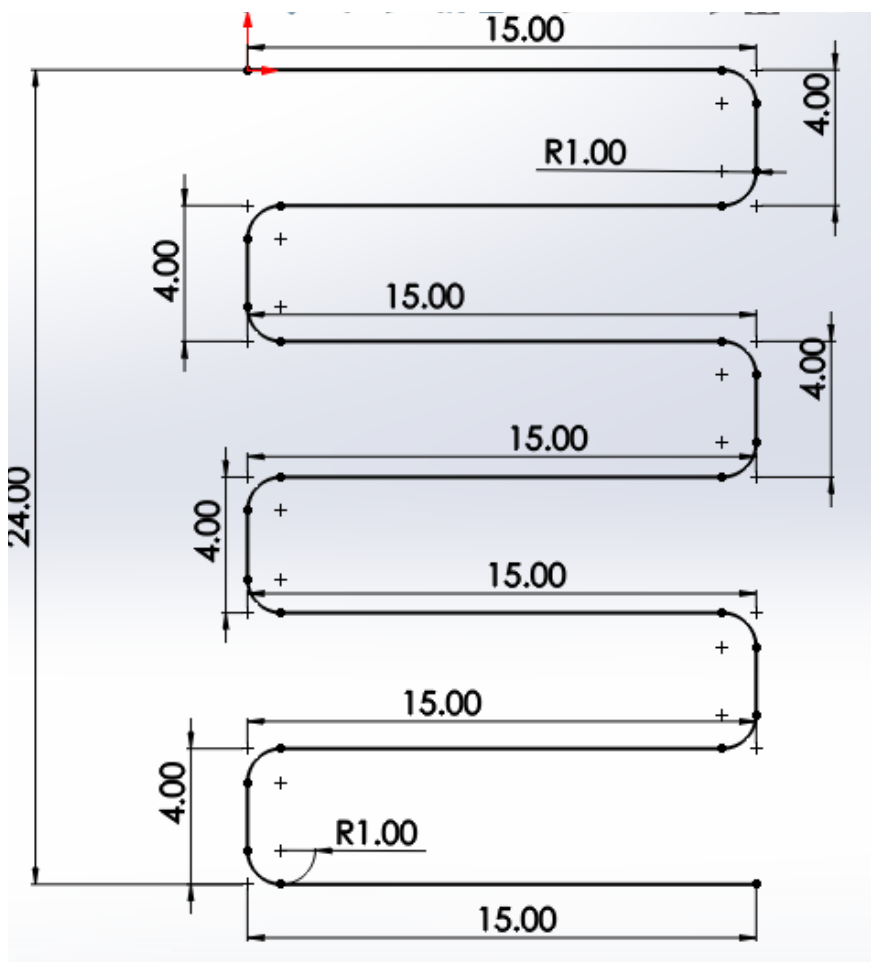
Croquis del primer modelo de la tubería, vista frontal.
